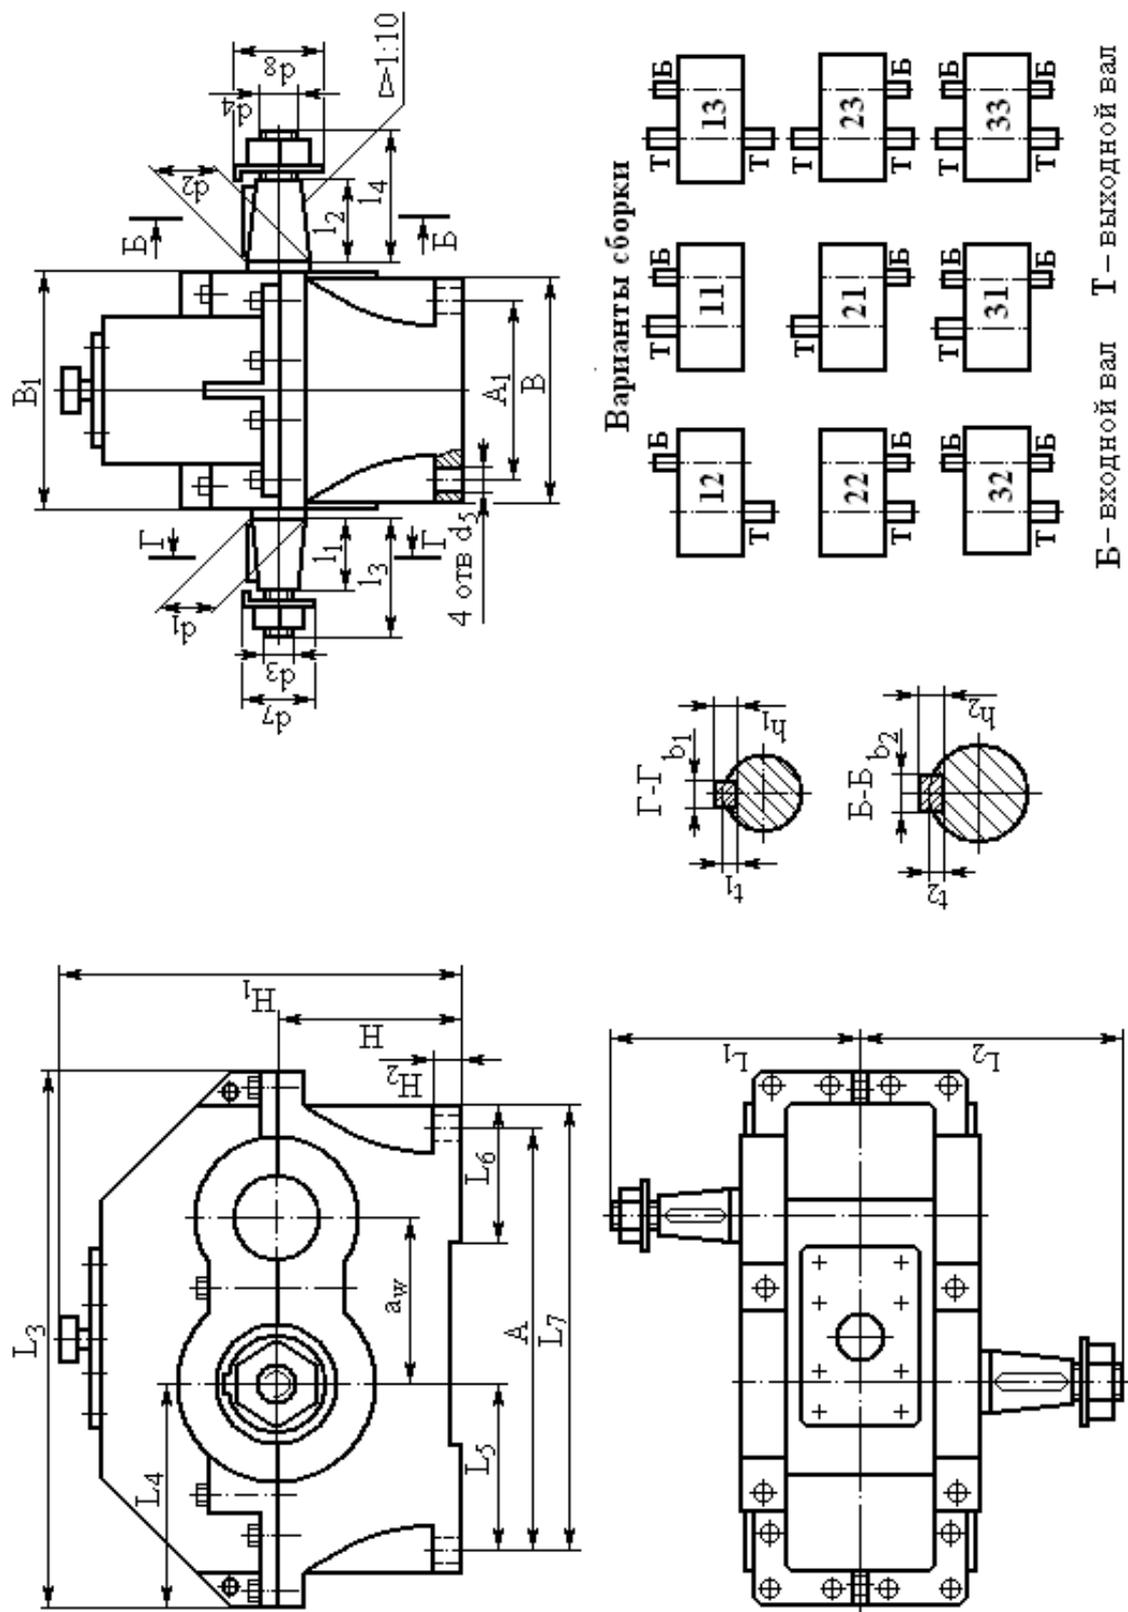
Цилиндрический одноступенчатый редуктор типа ЦУ
